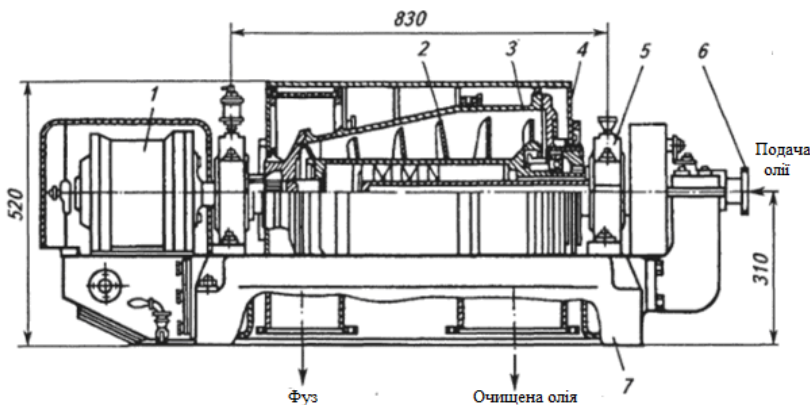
Центрифуга НОГШ-325: 1 - планетарний редуктор; 2 шнек; 3-ротор; 4-кожух; 5-підшипники; 6-живильна труба; 7-станина олії.
